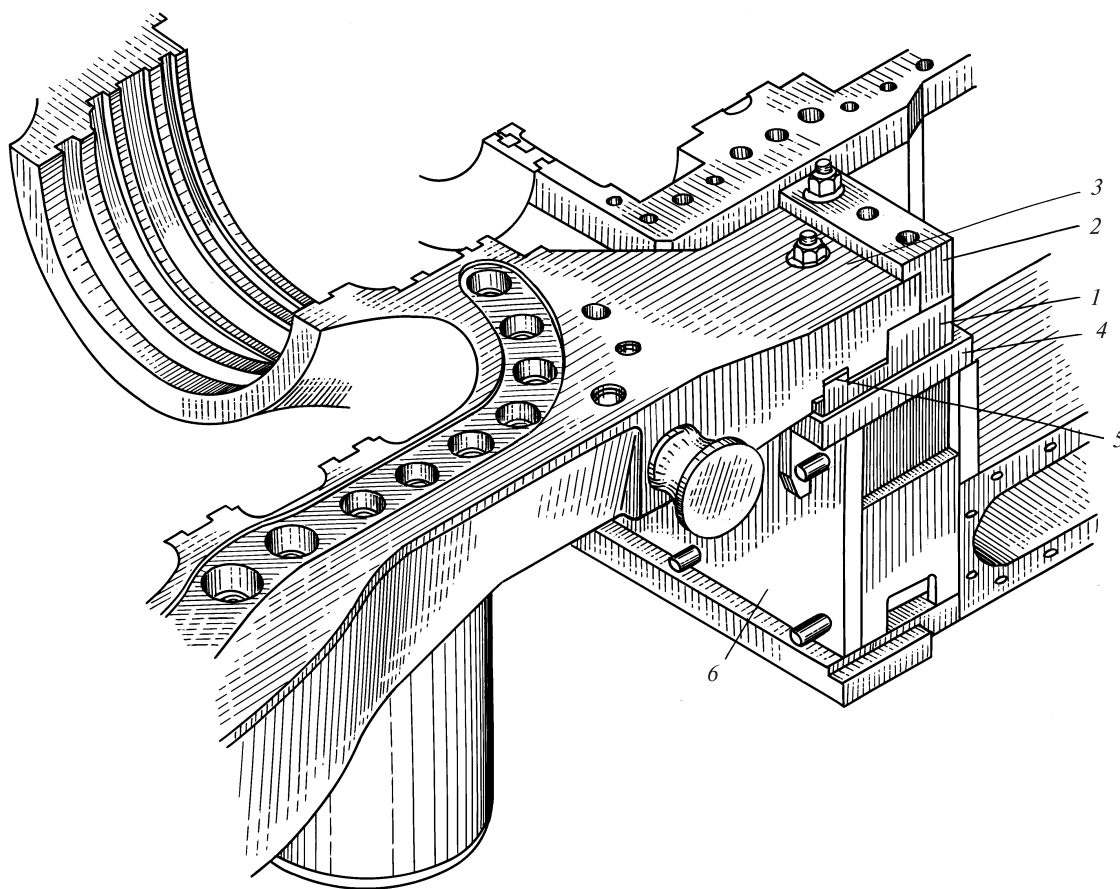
Опираие корпуса ЦВД турбины Т-250/300-23,5 ТМЗ на корпус среднего подшипника
